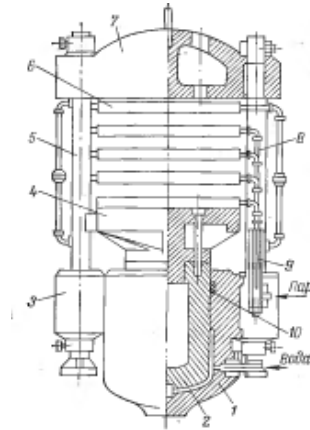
Багатополичний (поверховий) гідравлічний прес:
